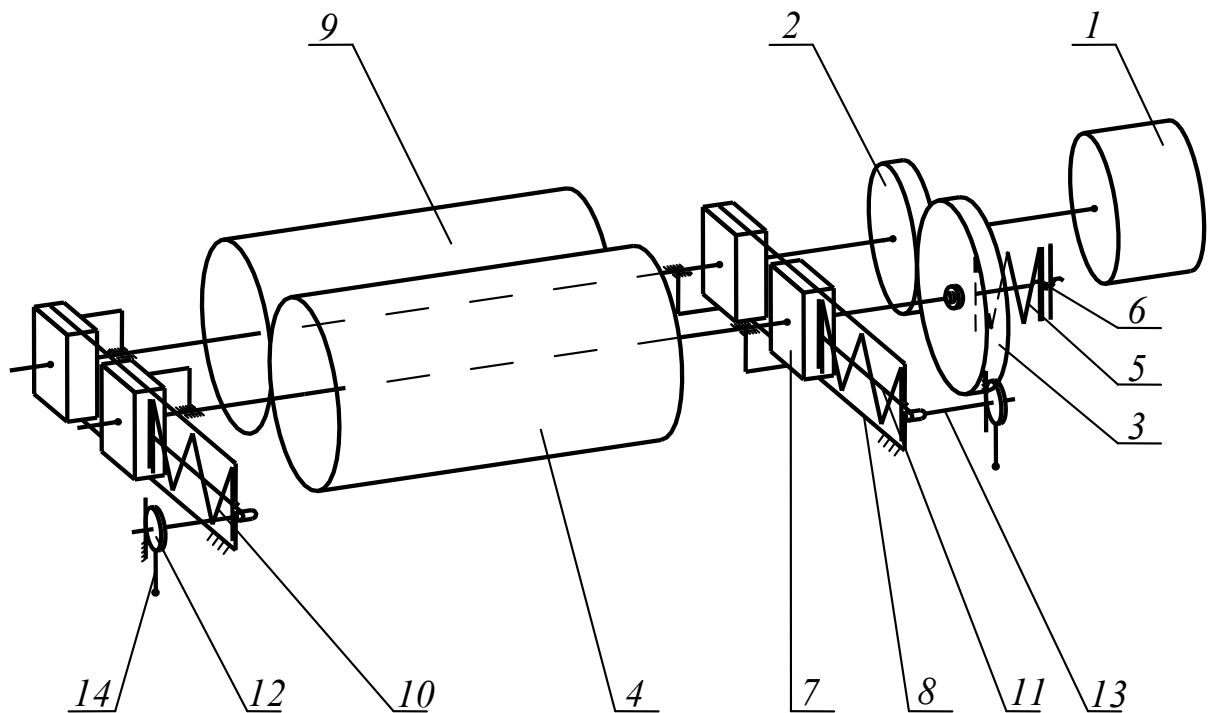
Кінематична схема механізму товарівідтягування
